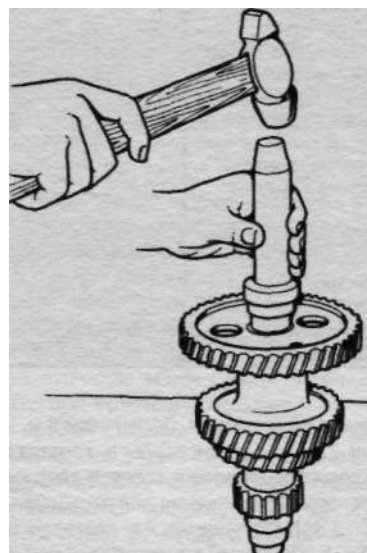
Напрессовка внутреннего кольца роликового подшипника промежуточного вала
